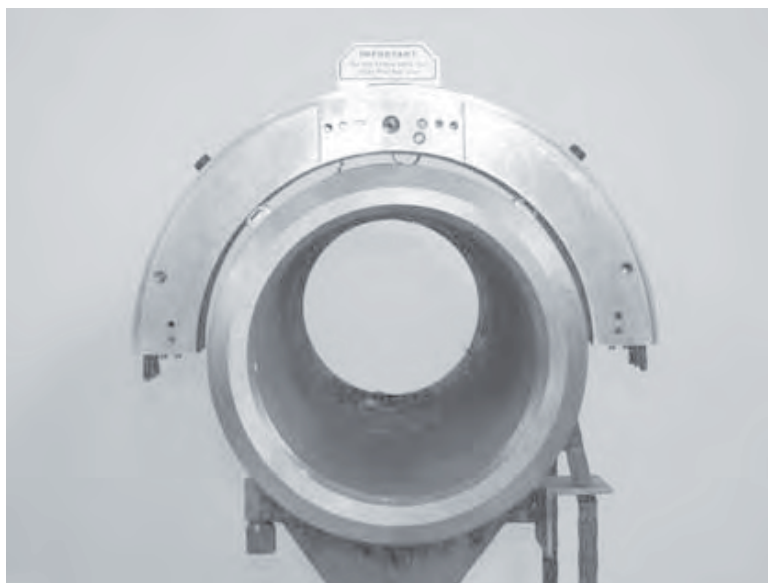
На горизонтальных трубах следует устанавливать агрегат стороной с корпусом ведущей шестерни в верхней части трубы.
